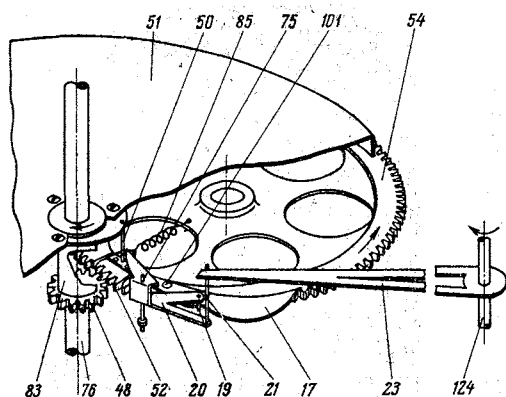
Кинематическая схема включения механизма смены пластинок: 17 — пластина; 19 — палец; 20 — рычаг; 21 — штифт; 23 — рычаг звукоусилителя; 48 — шестерня; 50 — штифт; 51 — маховик; 52 — сектор зубчатый; 54 — шестерня; 75 — ось; 76 — вал; 83 — полый вал; 85 — пружина; 101 — ось; винт М2,5×8; 124 — ось звукоусилителя.
